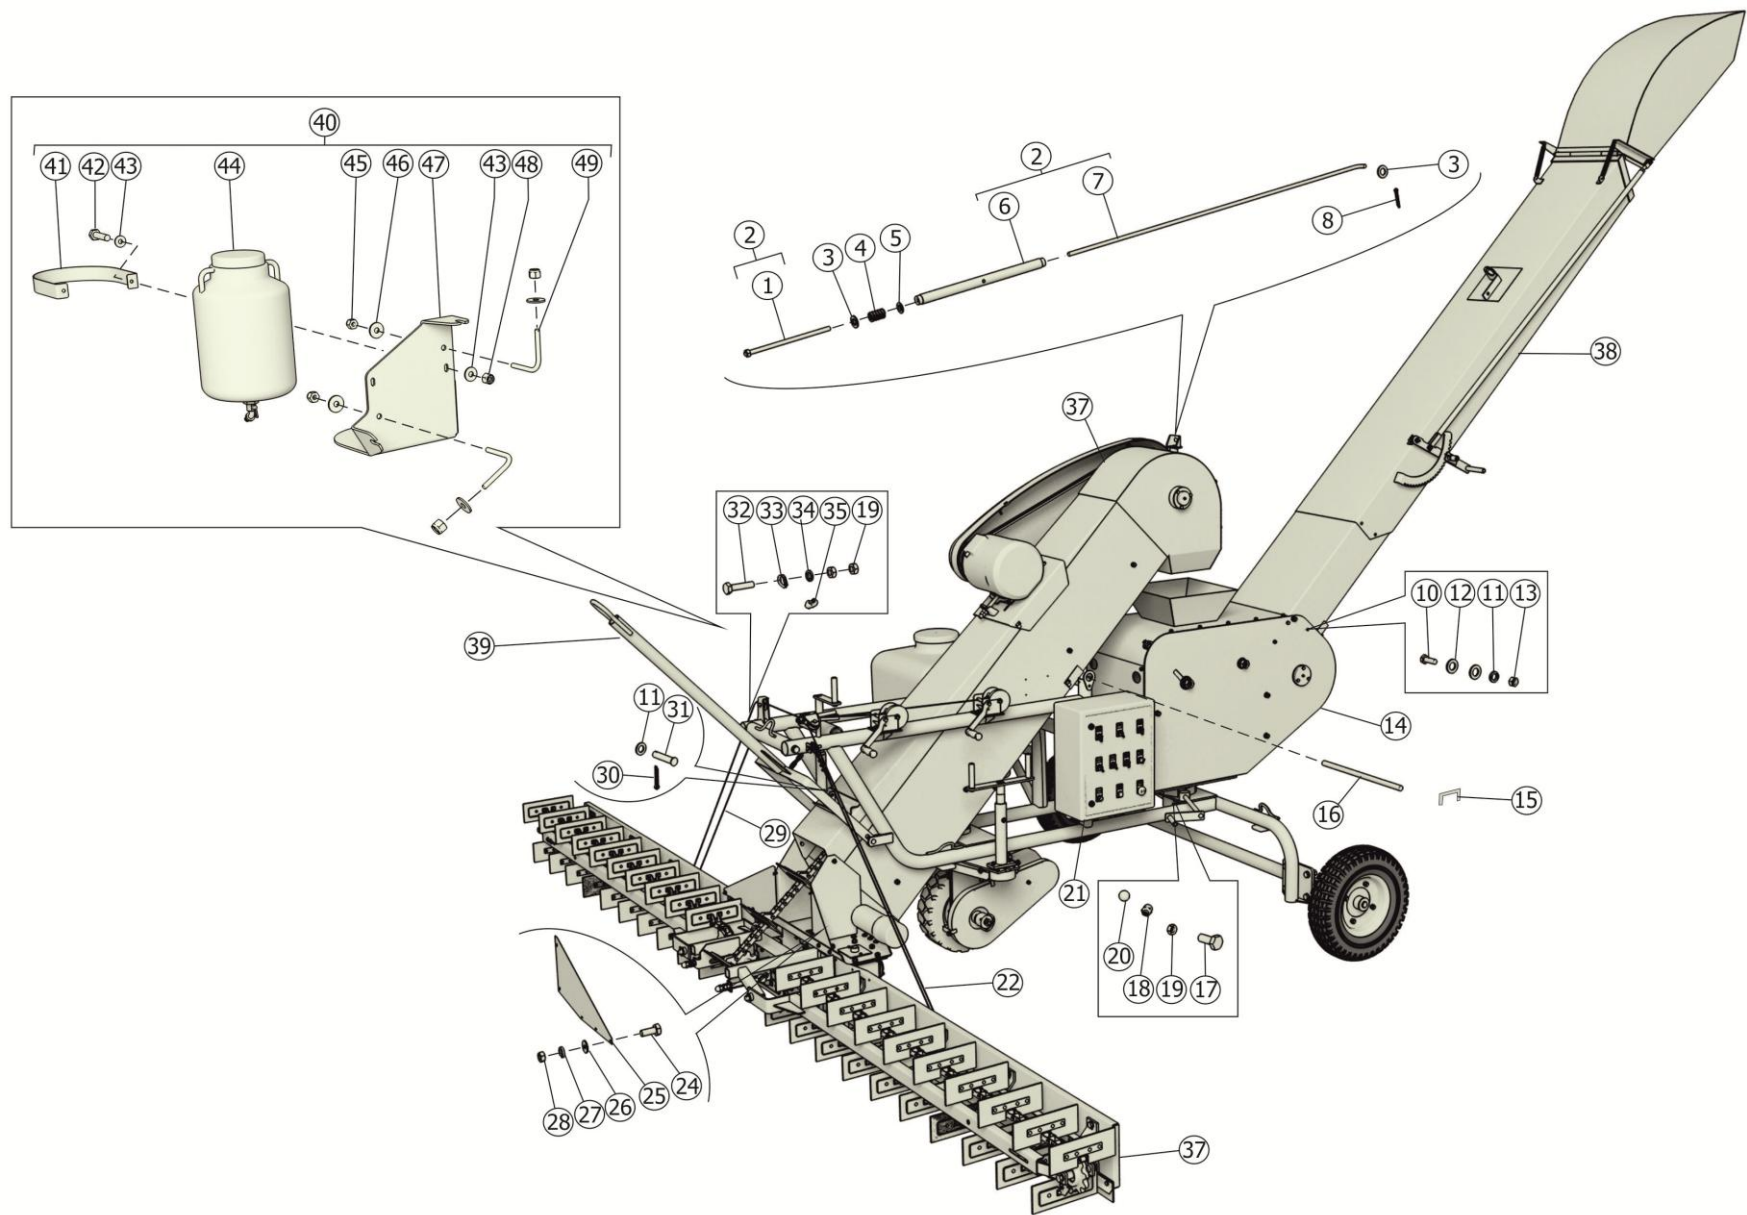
Комплекс зерноперерабатывающий ЗМП-ПСМ-05/-06. Общий вид
